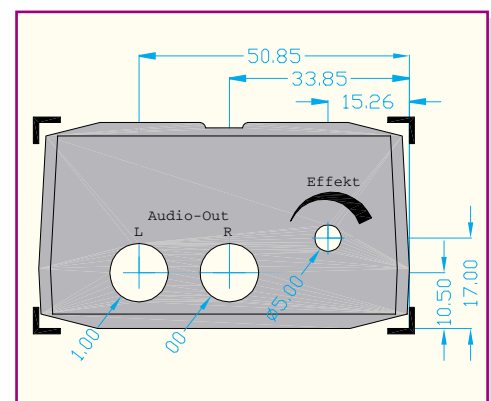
Maßzeichnung und Bedruckung der Gehäuserückwand
